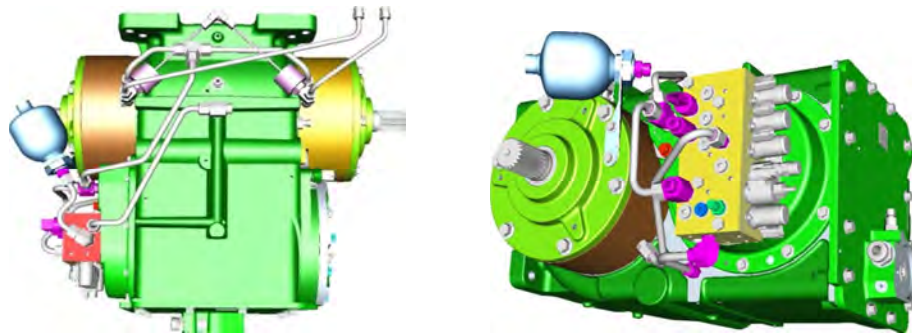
K EXPLOSIONADO DE PIEZAS CORRESPONDIENTE AL MONTAJE FINAL 6
